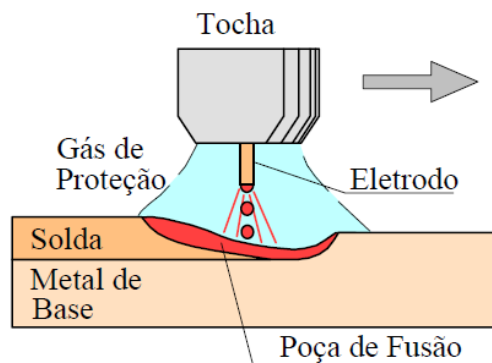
Desenho esquemático do processo de soldagem GMAW (MODENESI; MARQUES, 2006).
